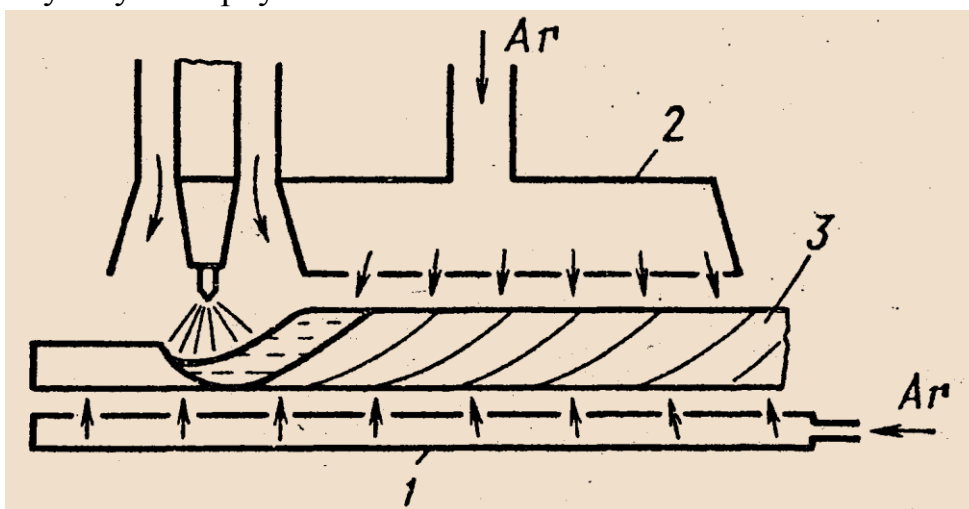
Горелка с удлиненной насадкой для аргоннодуговой сварки
